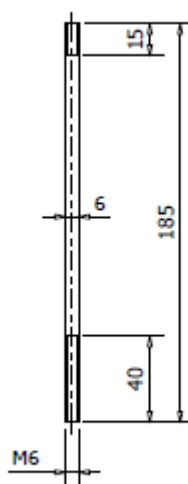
Prigionieri per fissaggio della lampada. Uniscono le due flange di chiusura.
